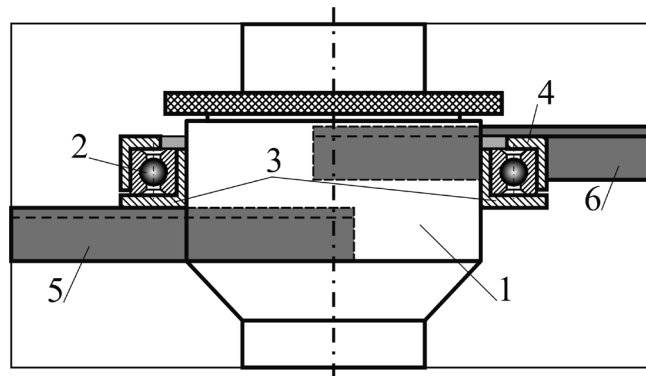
Схема размещения транспозиционного водовода на опорном каркасе
